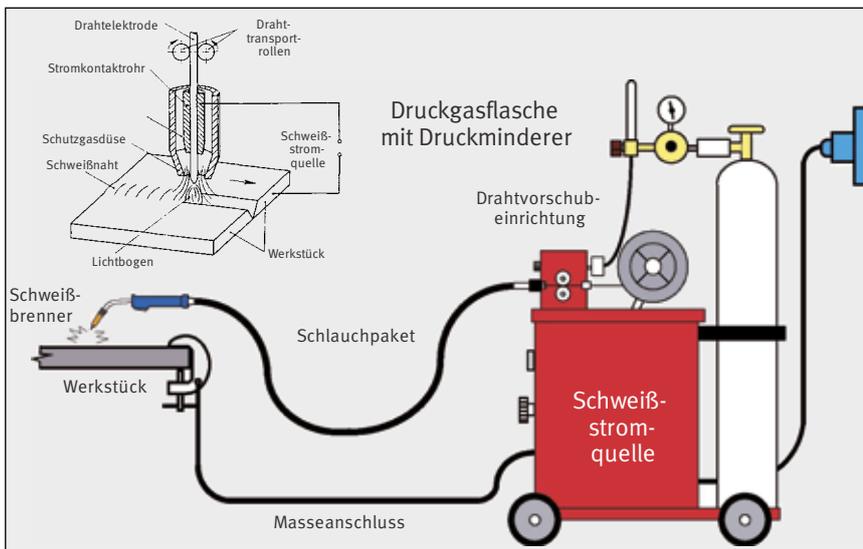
Schweißarbeitsplatz zum MSG-Schweißen
